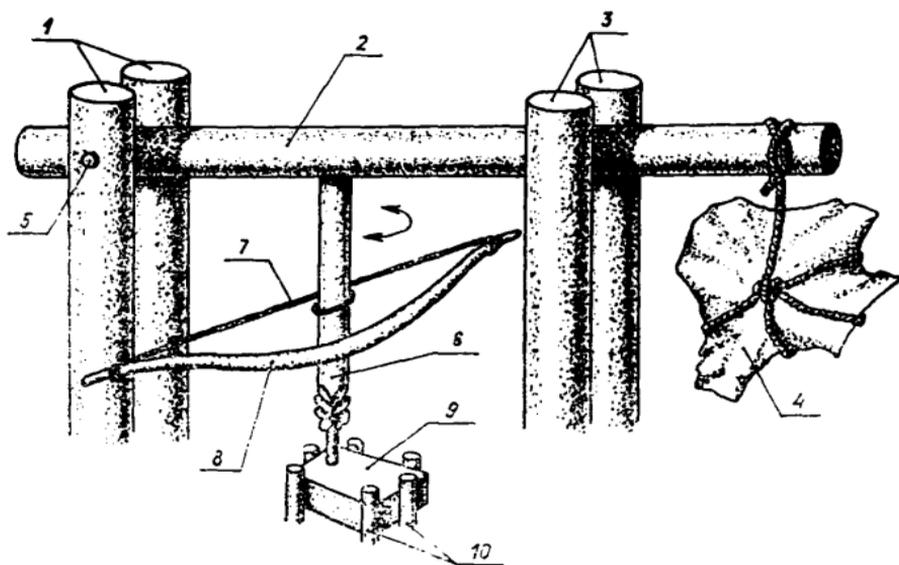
Первобытный станок для цилиндрического сверления каменных топоров.
